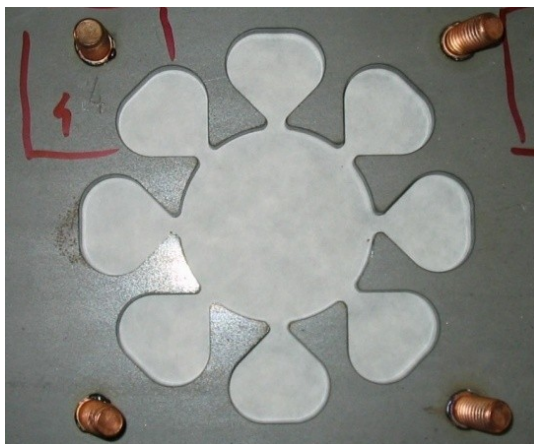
Detail polotovaru zkušebního spoje č. 3.
